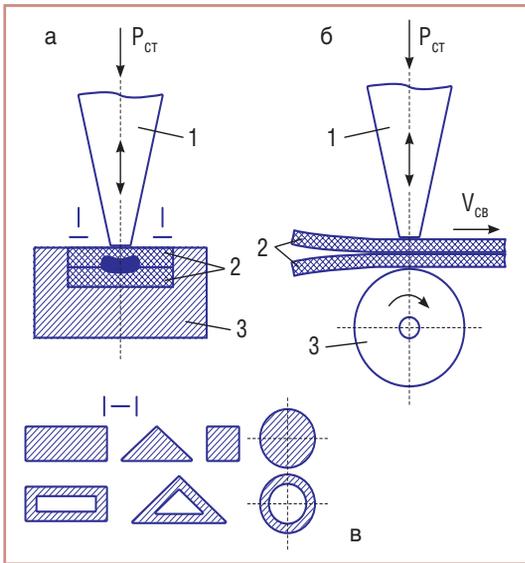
Схема контактной ультразвуковой сварки: а – прессовая; б – шовная; в – возможные формы рабочего торца волновода-инструмента (1 – волновод-инструмент; 2 – свариваемые детали; 3 – опора)
